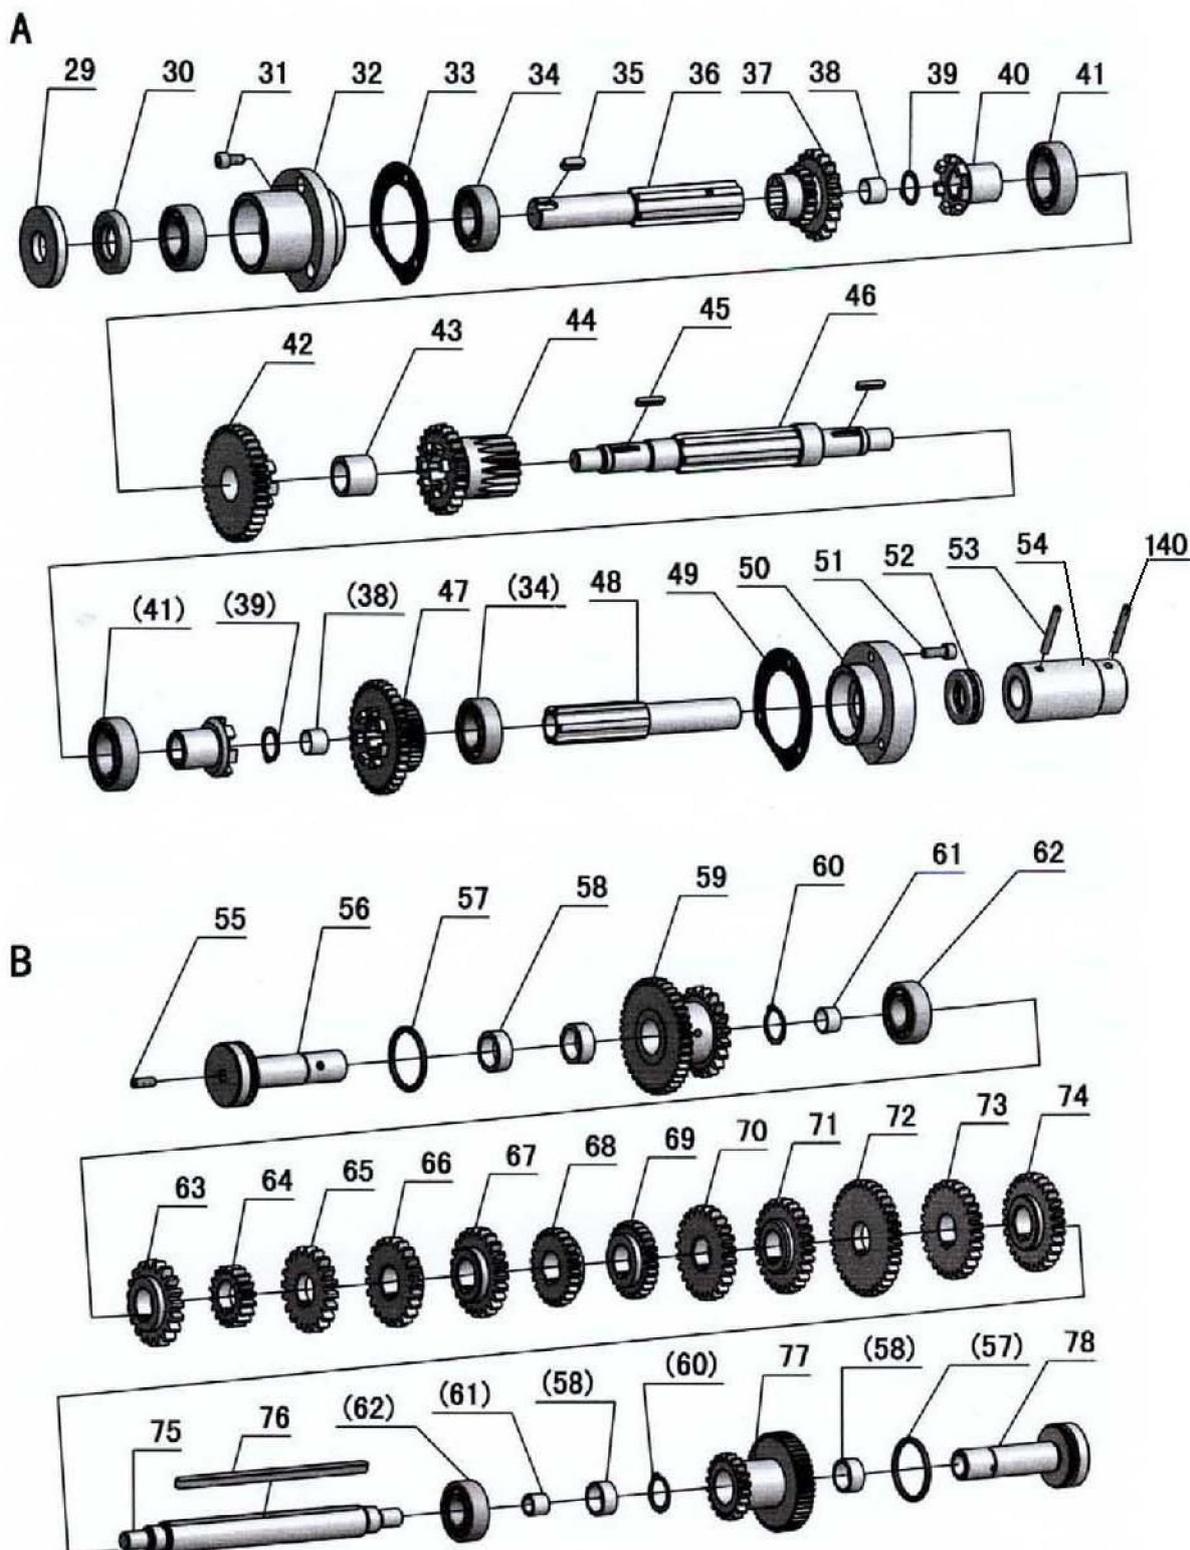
Vorschubgetriebe 2 von 4 – Engranaje de avance del cabezal 2 de 4
